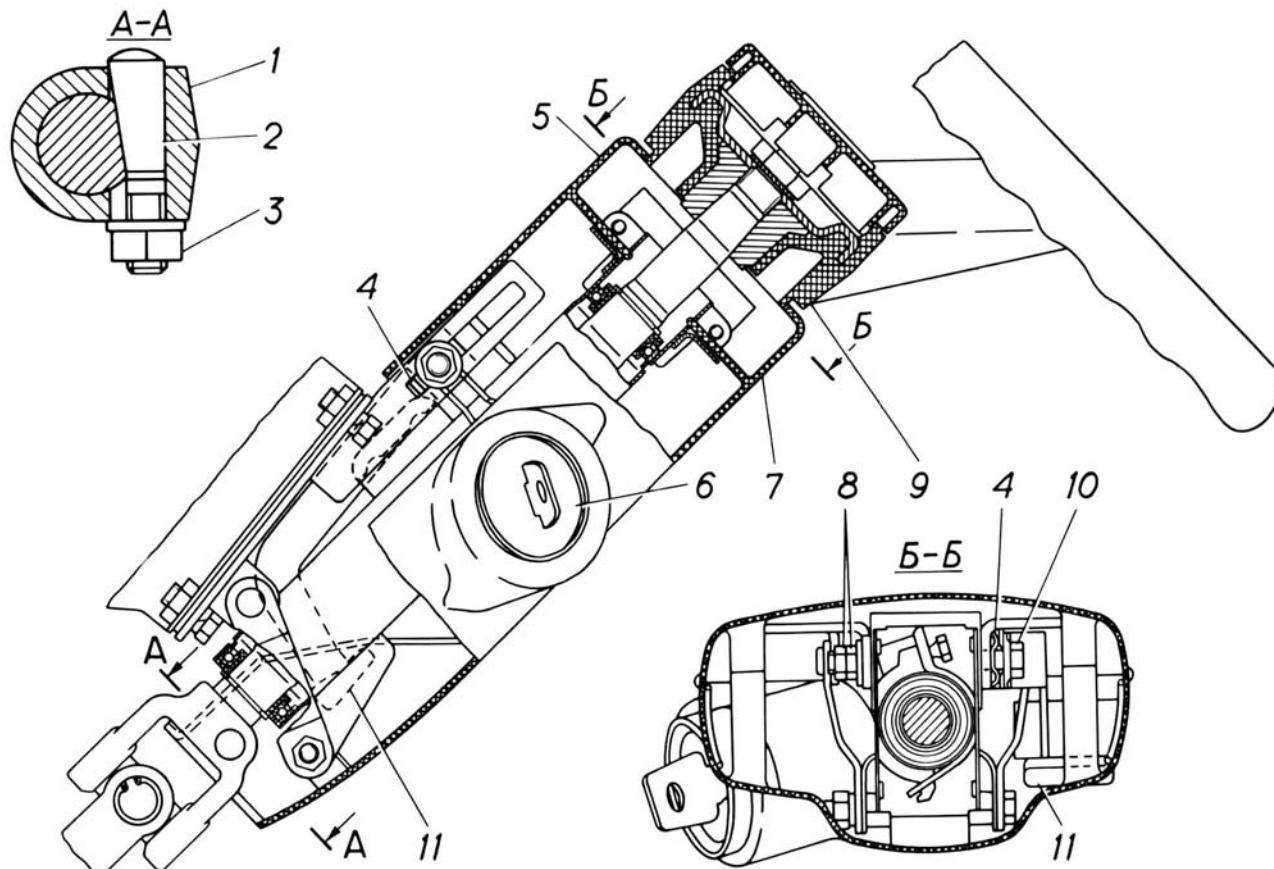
Рулевое колесо и колонка: 1 – вилка карданного вала; 2 – клин; 3 и 8 – гайки; 4 – упорная шайба; 5 – верхний кожух; 6 – выключатель зажигания; 7 – нижний кожух; 9 – рулевое колесо; 10 – болт; 11 – рукоятка
